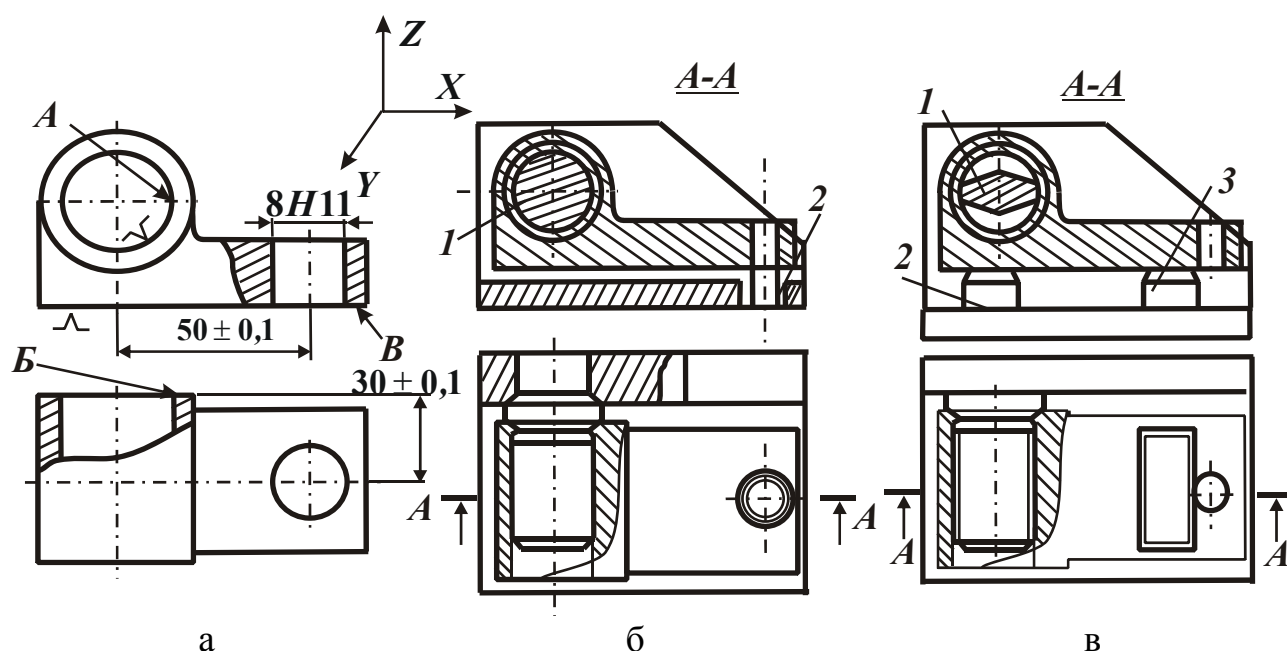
Варианты базирования заготовки двумя плоскостями и одним отверстием.
